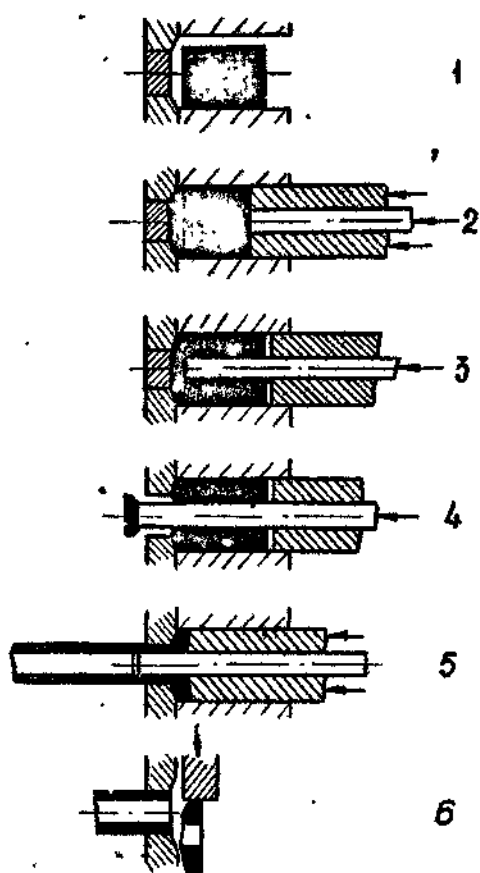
Технологические операции при прессовании труб: 1 – загрузка заготовки в контейнер; 2 – распрессовка заготовки; 3 – прошивка иглой; 4 – удаление донной части; 5 – прямое прессование трубы; 6 – удаление прессостатка
